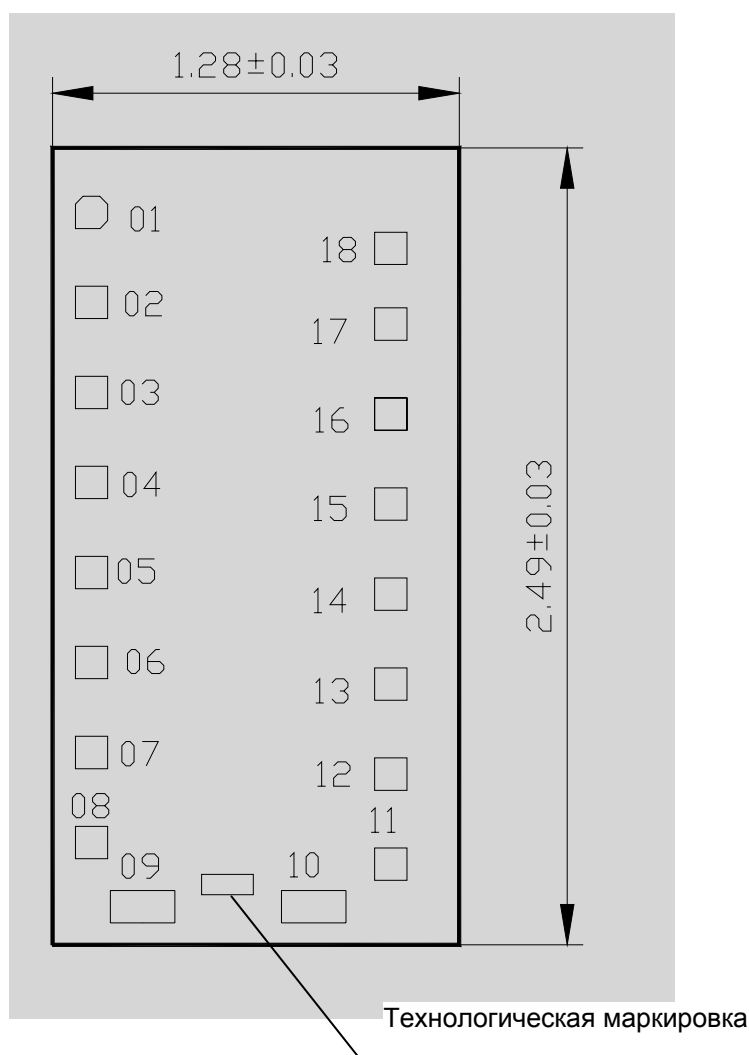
Габаритный чертеж корпуса MS-001AC
